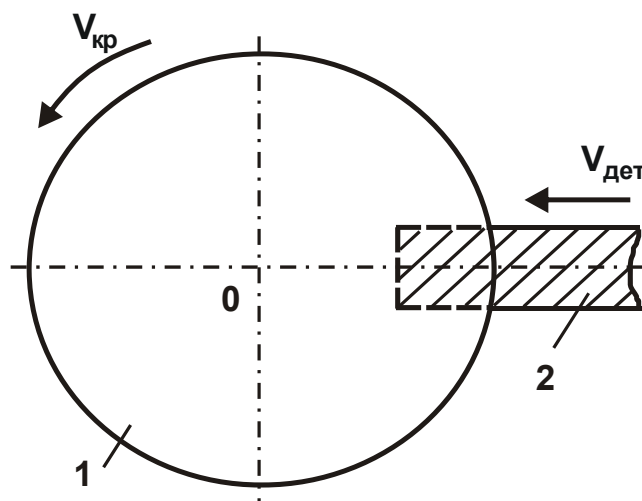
Расчетная схема процесса шлифования прямолинейной детали: 1 – круг; 2 – обрабатываемая деталь
